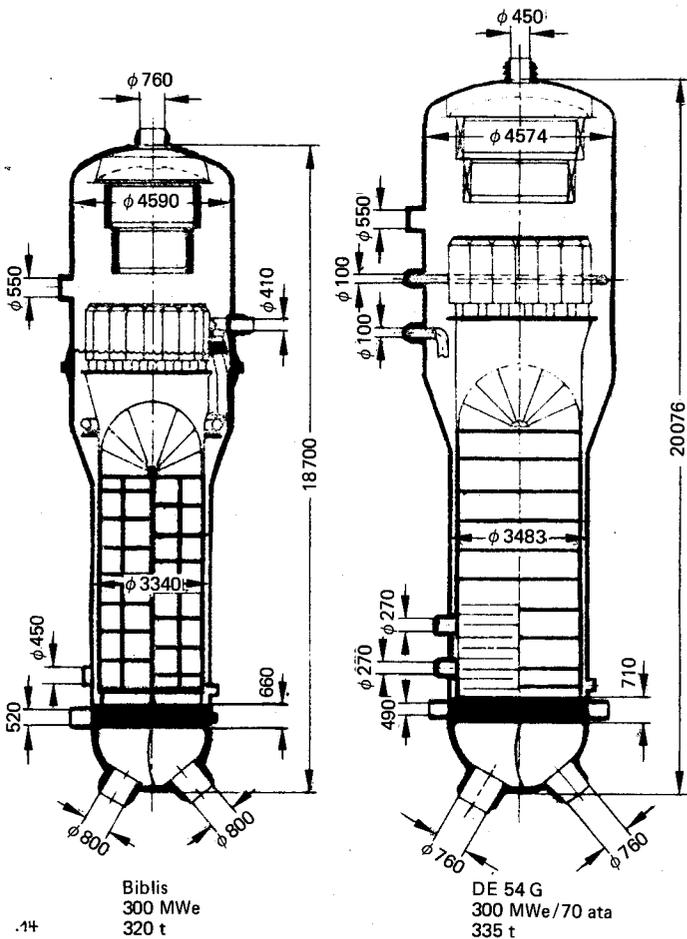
Dampferzeuger für Druckwasserreaktoren.
